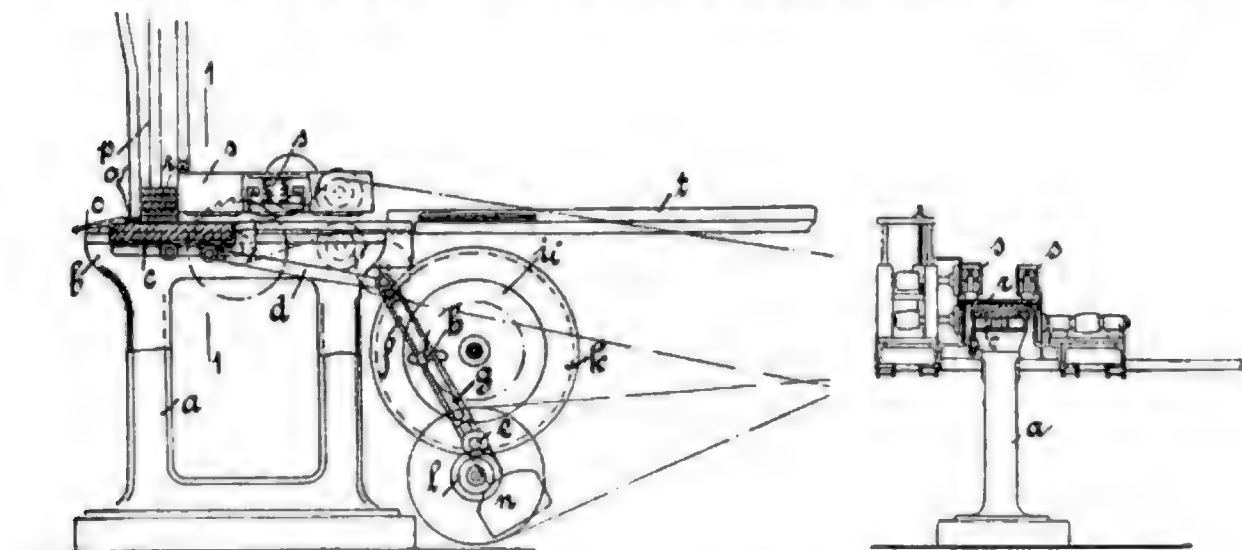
Parquettenbearbeitungsmaschine. (Seitenansicht.)
